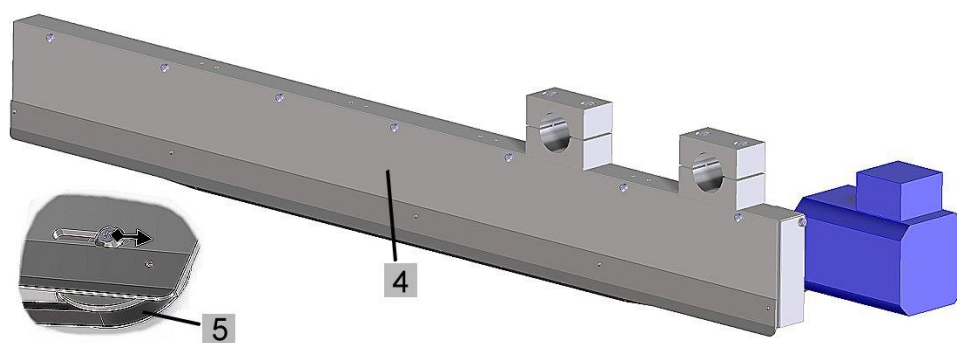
tension de la courroie et montage de la tôle latérale
